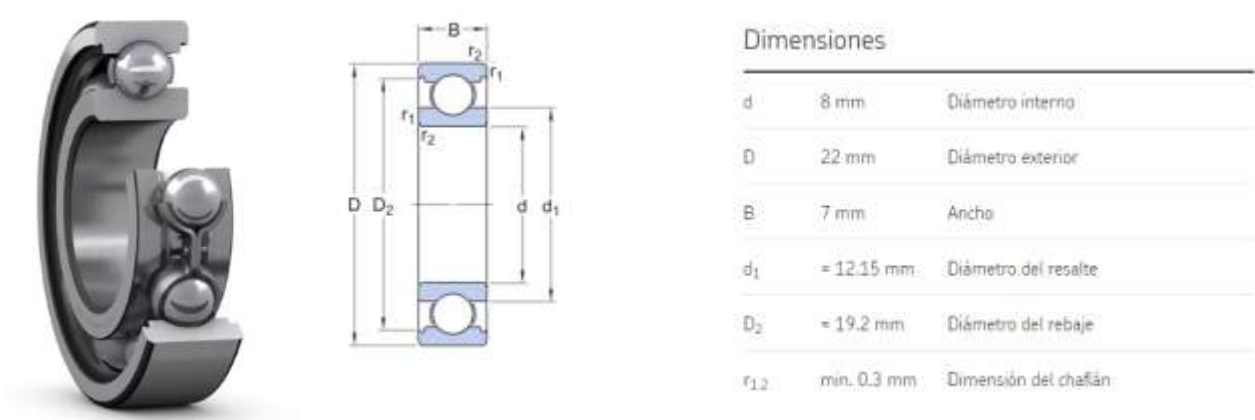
Dimensiones del Rodamiento Rígido de Bolas 608
